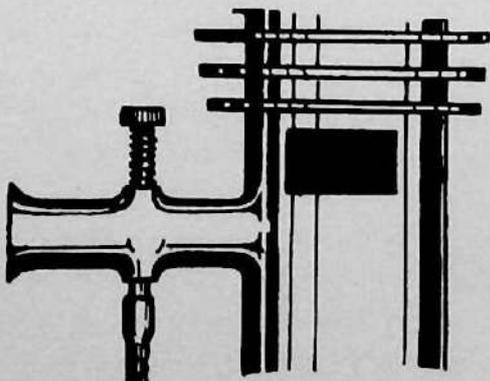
a. Su molti motori il carburatore è fissato posteriormente.
